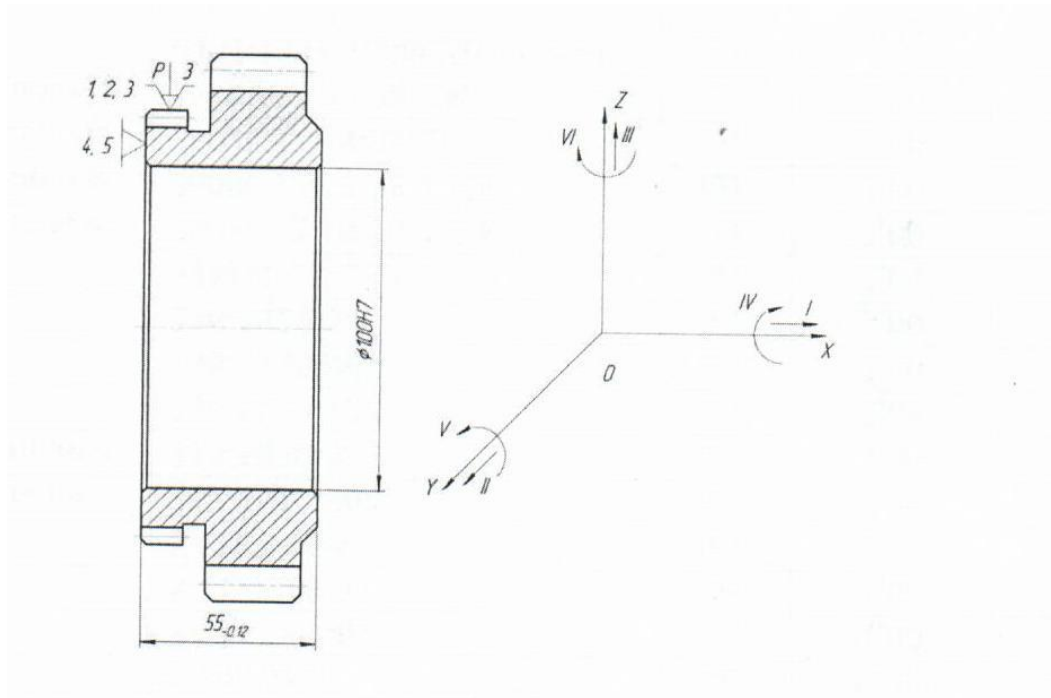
Схема базування заготовки шліфування на внутрішньо-шліфувальному верстаті
